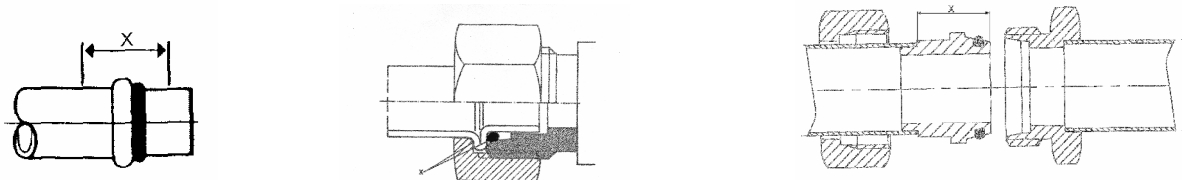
O-Ring - Anschlüsse an Block – Expansionsventil für Rohr- und Schlauchanschlüsse
